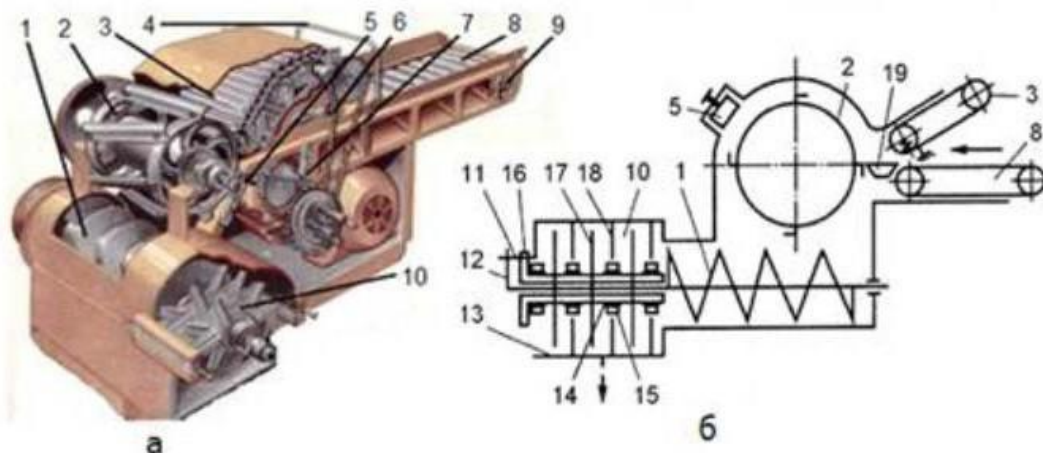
Загальна будова (а) та конструктивно-функціональна схема (б) шнекового подрібнювача ИКВ-5А: 1 – шнек; 2 – ножовий барабан; 3 – похилий конвеєр; 4 – механізм керування конвеєрами; 5 – натяжний пристрій ланцюгового передавача редуктора; 6 – натяжний пристрій ланцюгового передавача похилого конвеєра; 7 – натяжний пристрій ланцюгового передавача горизонтального конвеєра; 8 – горизонтальний конвеєр; 9 – натяжний пристрій горизонтального конвеєра; 10 – подрібнювальний апарат другого ступеня; 11 – зрізний штифт; 12 – фланець вала шнека; 13 – опора нерухомих ножів; 14 – прокладка; 15 – кільце; 16 – втулка; 17 – рухомий ніж; 18 – нерухомий ніж; 19 – протирізальна пластина.
